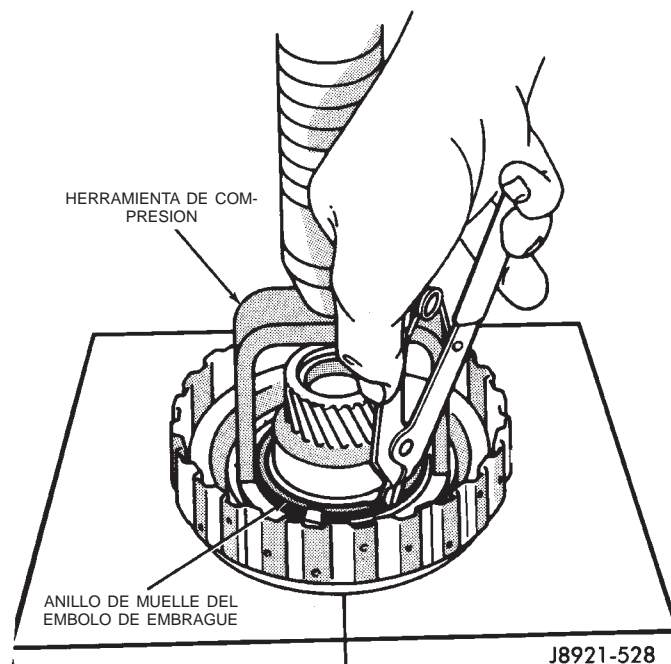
Desmontaje del anillo de muelle del émbolo de embrague
